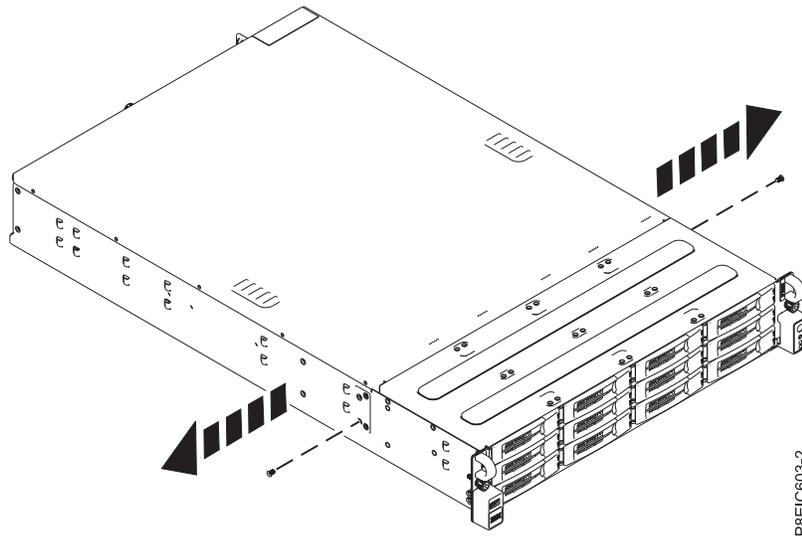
Schrauben der DASD-Rückwandplatine entfernen
